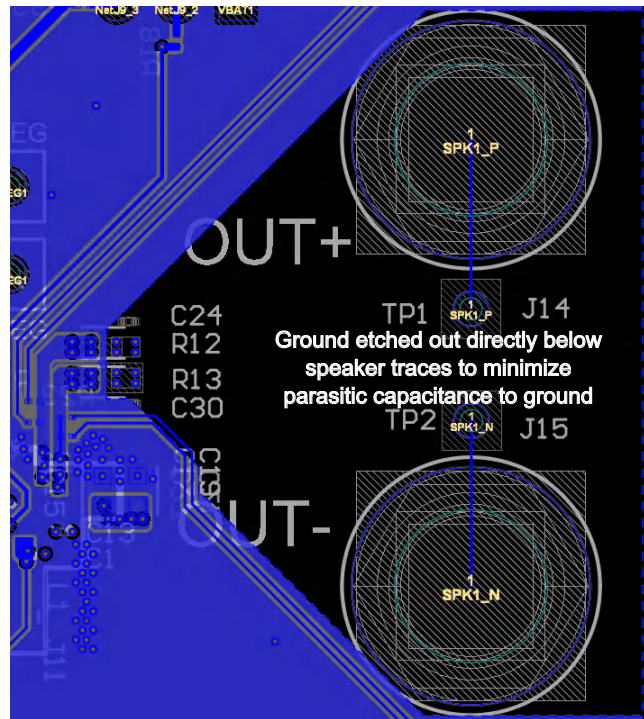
内部 PCB 层中 OUT\_P/N 路径下方的布线
